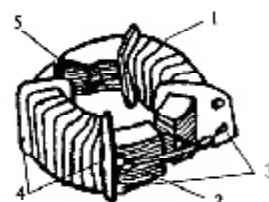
Магнитная головка: 1 — обмотка; 2 — сердечник из феррита; 3 — шпильки обмотки; 4 — каркас; 5 — передний (рабочий) зазор
